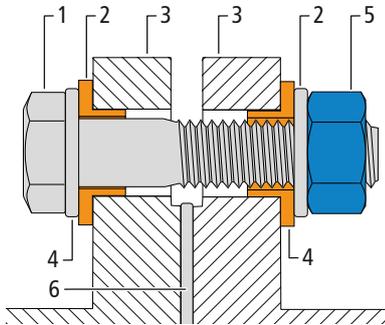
Assemblage par bride vissé avec douilles à colerette
